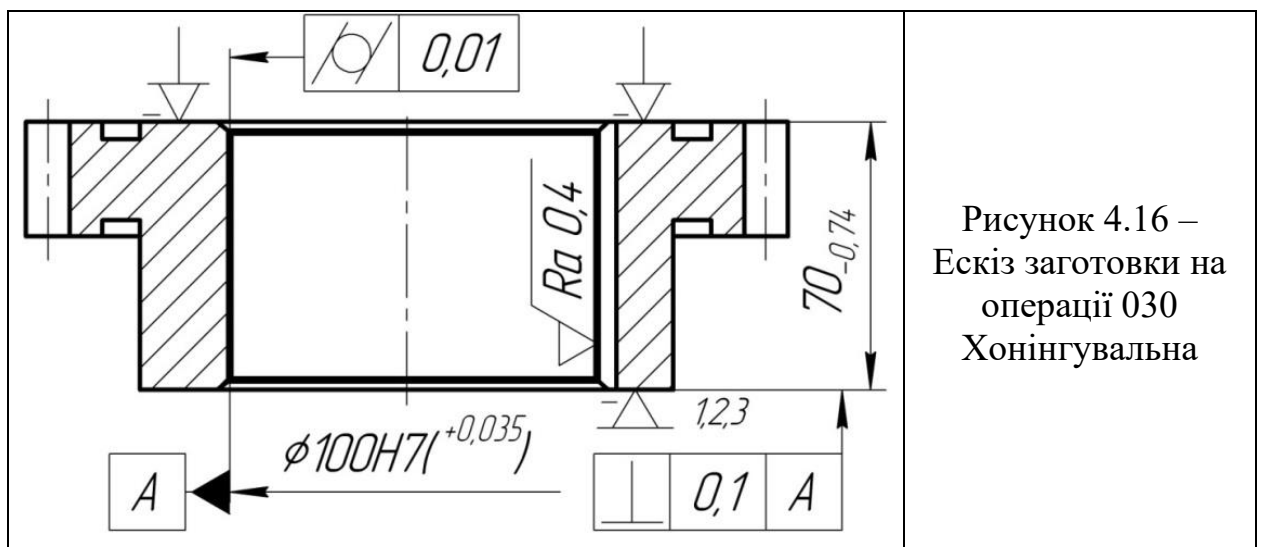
Ескіз заготовки на операції 030 Хонінгувальна
